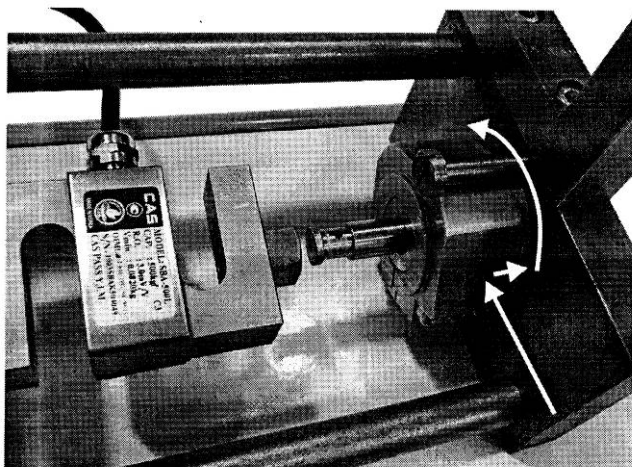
Установка втулки с валом в прессовое устройство
